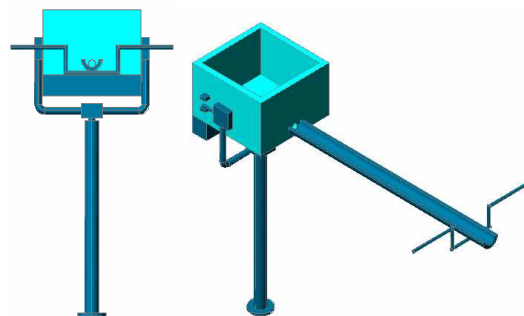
Imagen frontal y 3D del accesorio para llenado de moldes.
